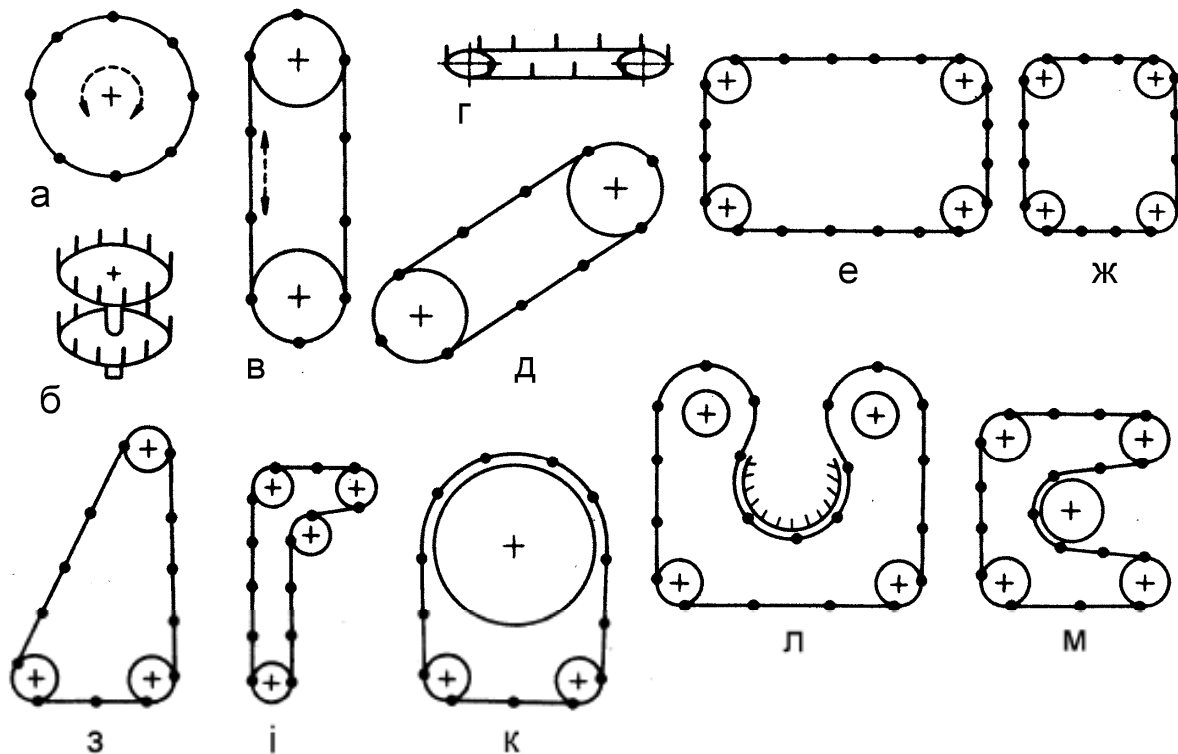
Інструментальні магазини багатоопераційних верстатів:
